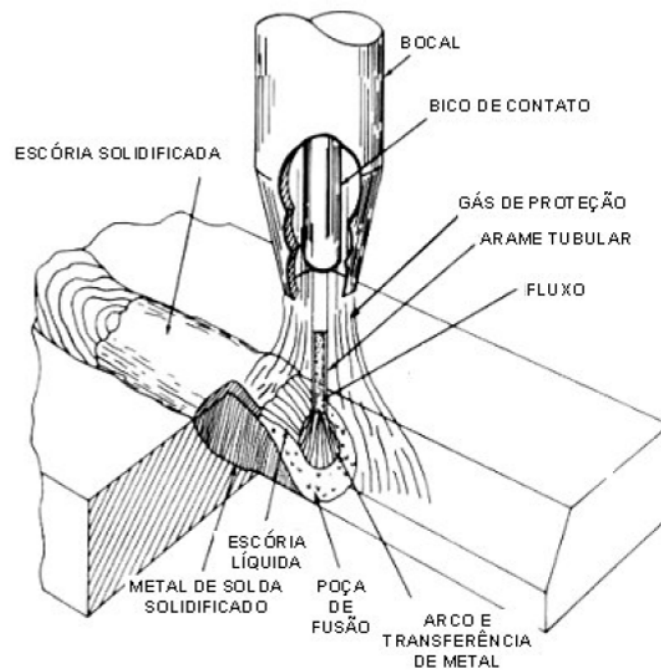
Soldagem com arame tubular com gás de proteção (FORTES, 2004)
